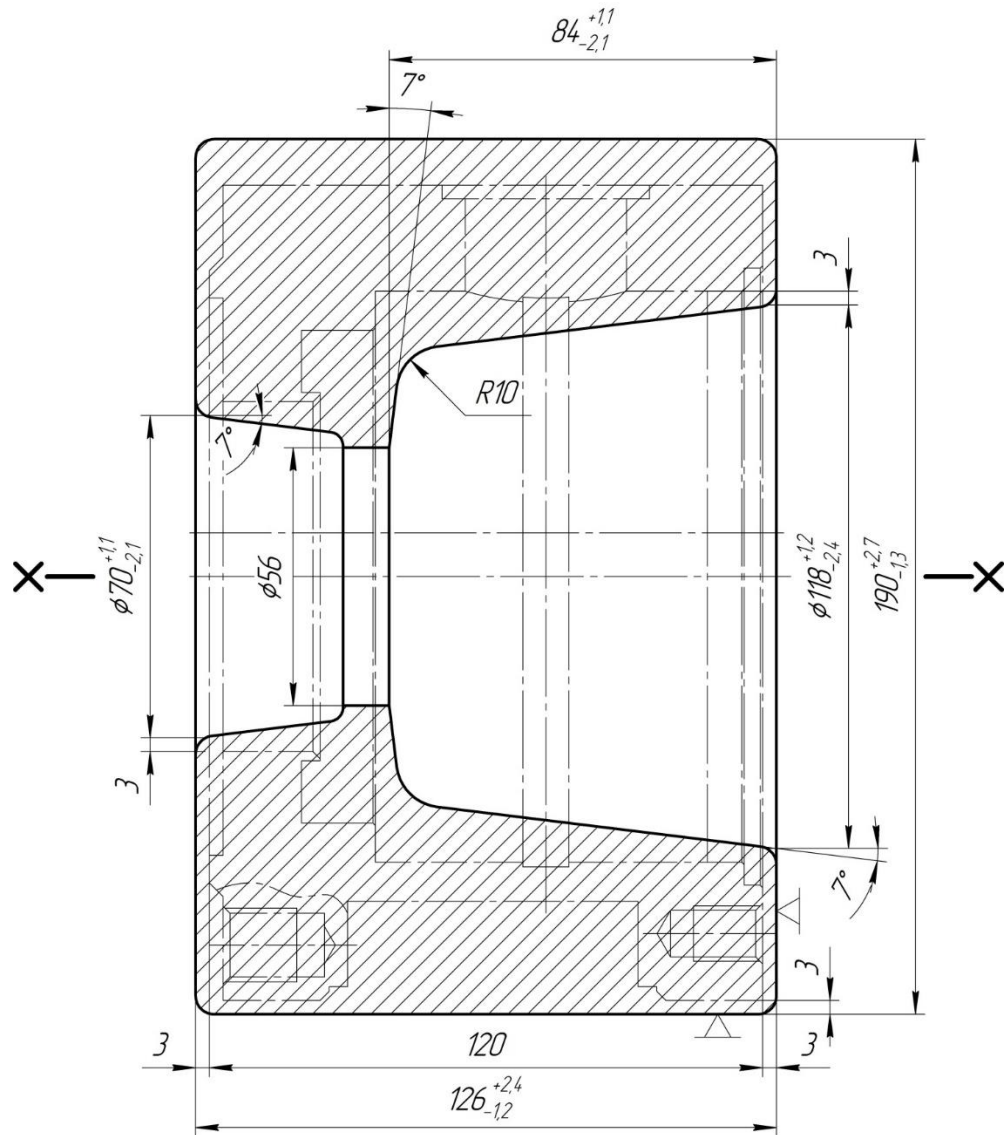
Креслення заготовки корпусу штампованого на КГШП
